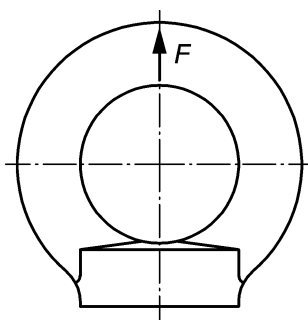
Beispiel für Kennzeichnung von Ringmuttern
